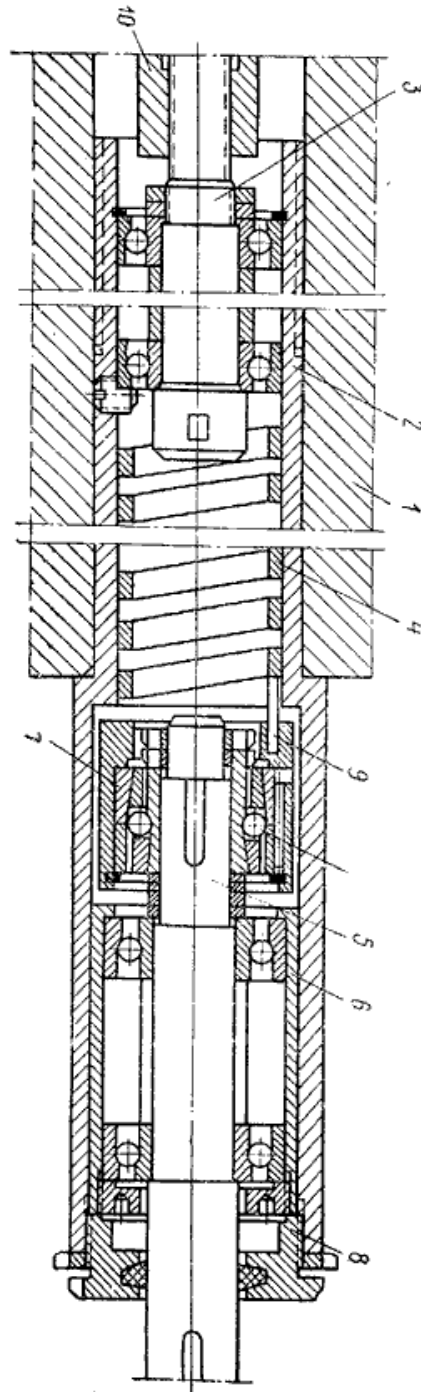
Механізм нерівномірної подачі шпинделя свердлильного верстата.[17]
